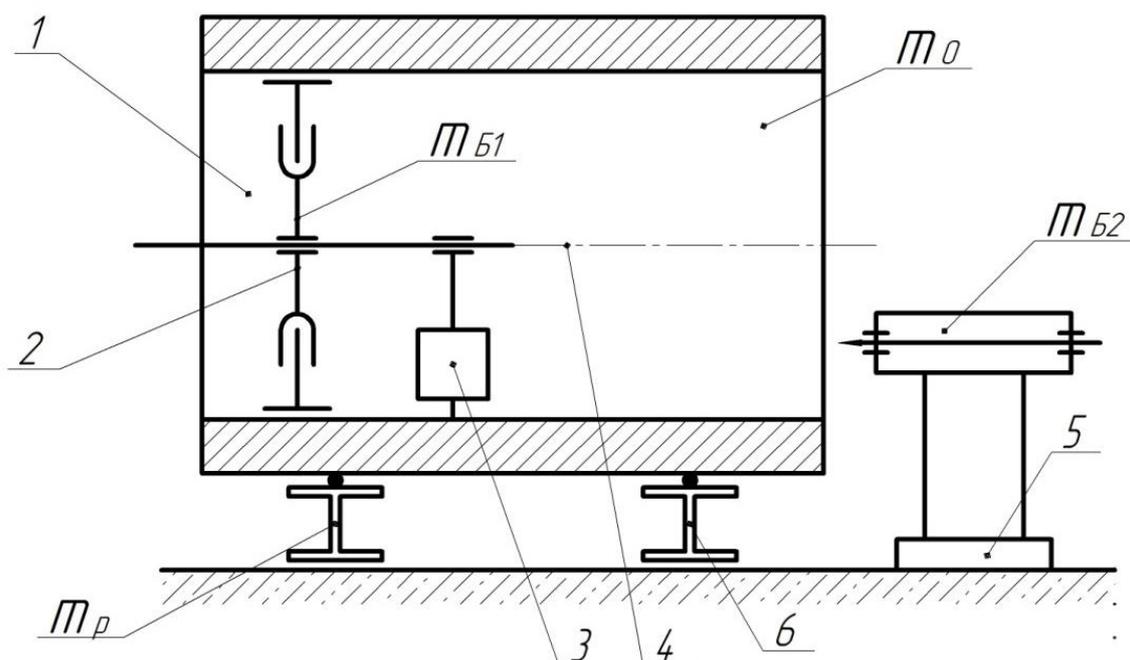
Проектная модель обработки обечайки на роликоопорном стенде с мобильными металлорежущими блоками. 1 – обечайка, 2 – опорный блок; 3 – блок обработки; 4 – базовая траверса; 5 – блок обработки торца; 6 – ролик опоры.
